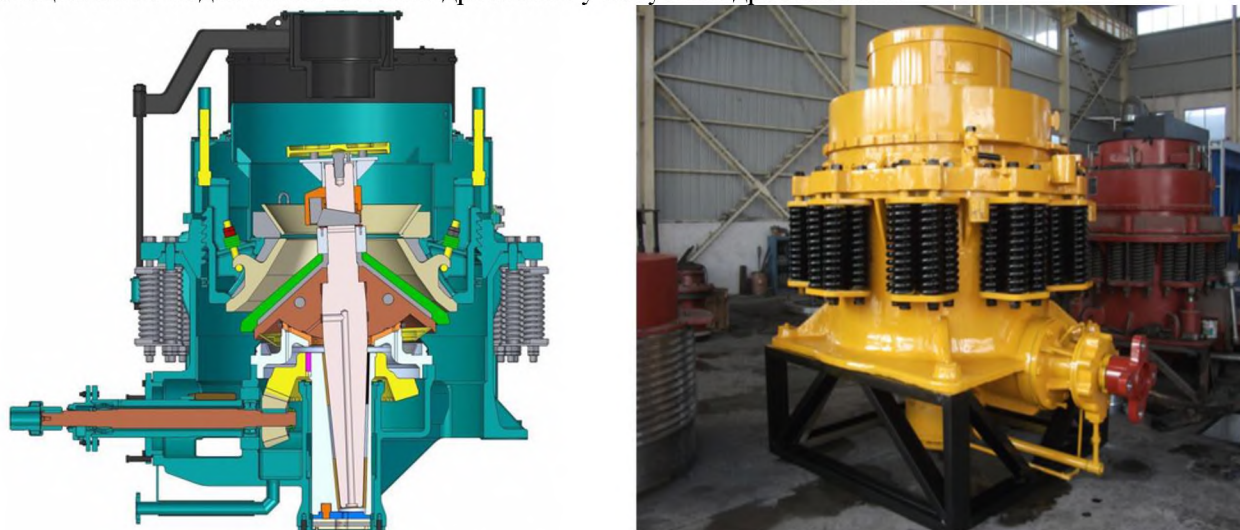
Конусная дробилка среднего дробления: конструкция и внешний вид
